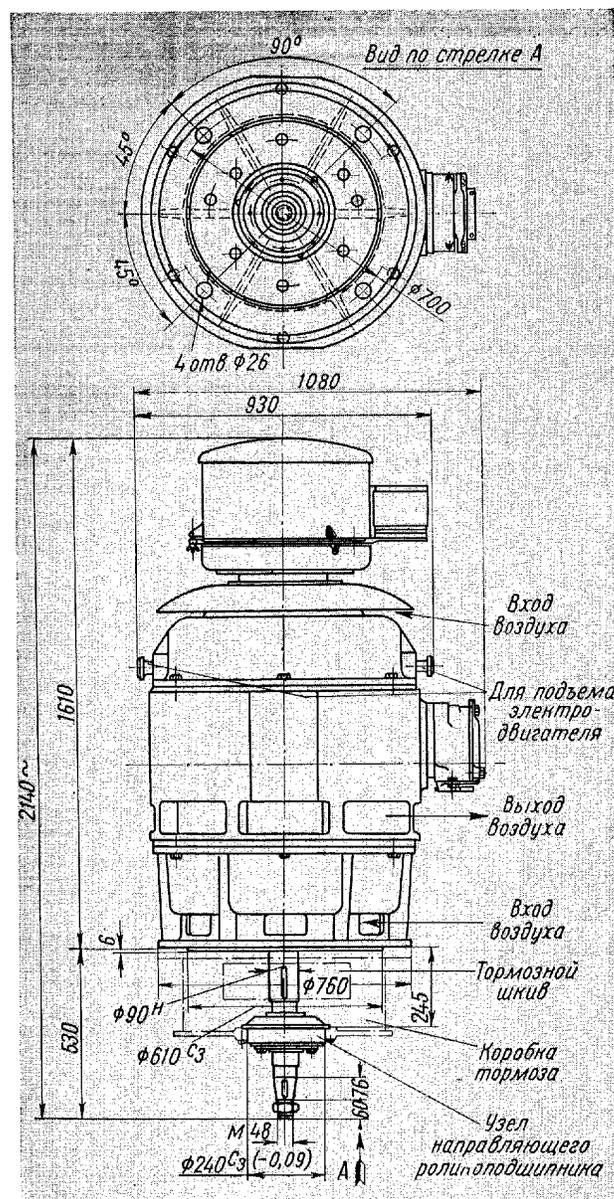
Размеры электродвигателя АМВЭ 126-6
